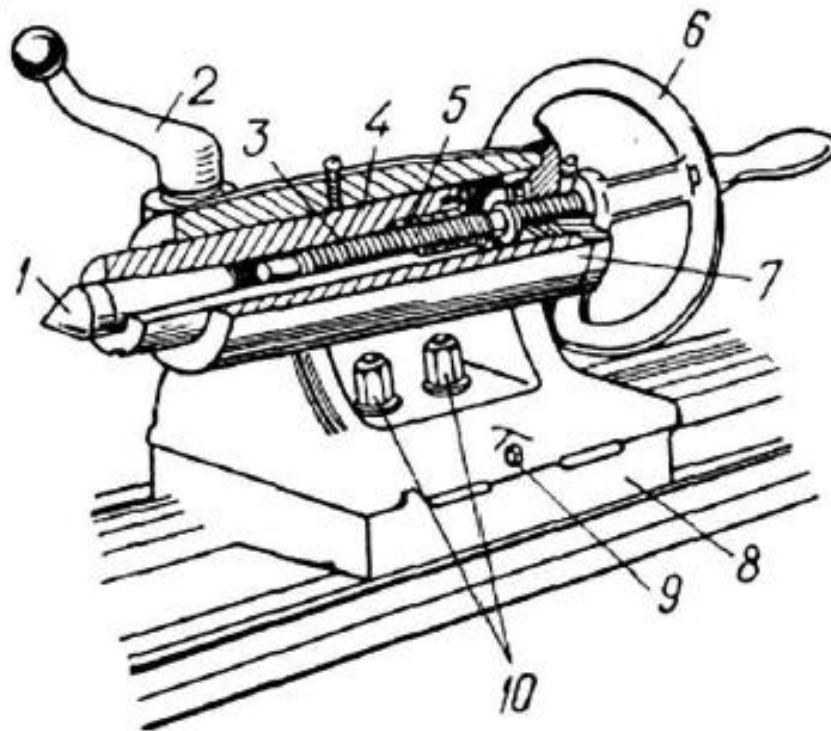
Задня бабка: 1 – центр; 2 – рукоятка; 3 – гвинт; 4 – піноль; 5 – різьбова втулка; 6 – маховичок; 7 – корпус; 8 – плита; 9 – гвинт; 10 – гайки.
